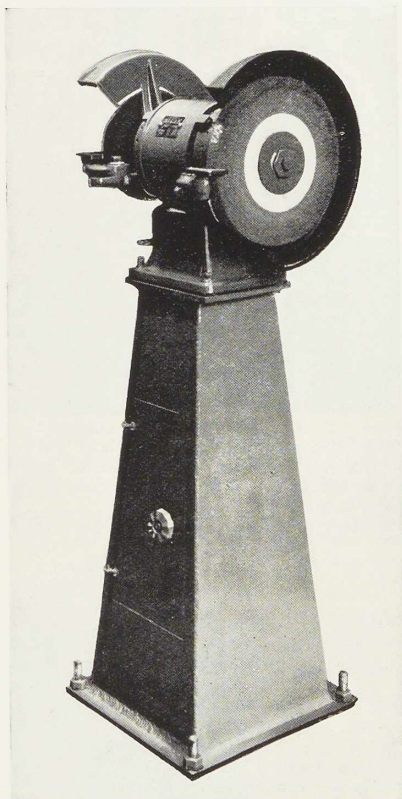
Bâti de meule en tôles d'acier assemblées par soudure oxyacétylénique.
